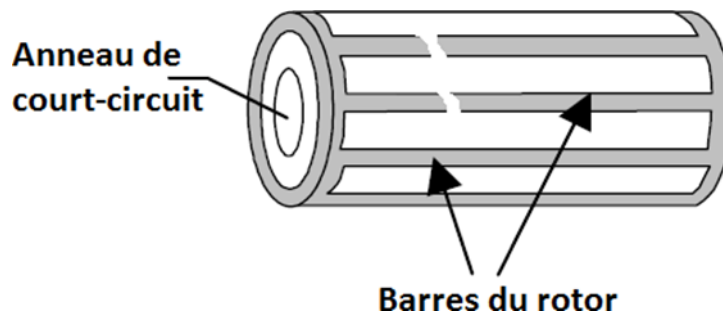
Défaut d'un rotor à cage d'écureuil, rupture de barres
